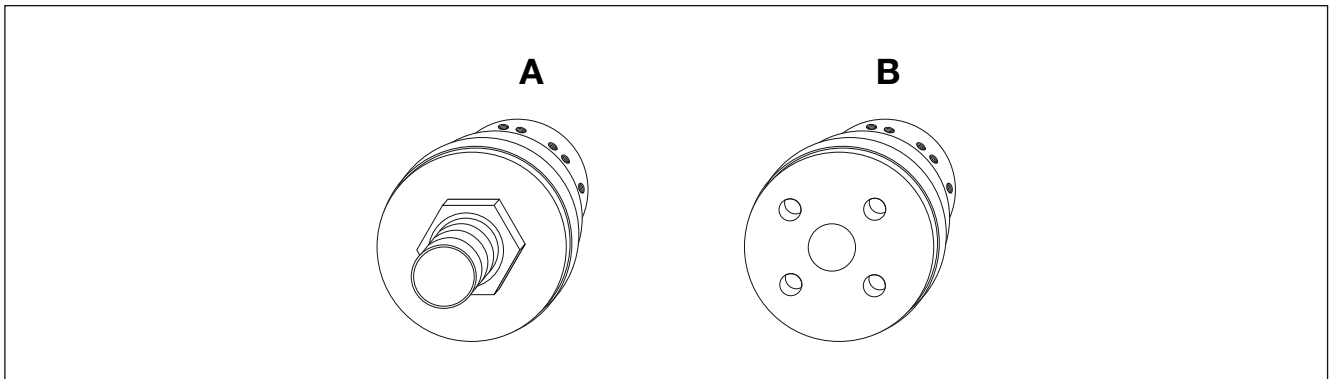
Variantes de fixation sur l'arbre de la machine
